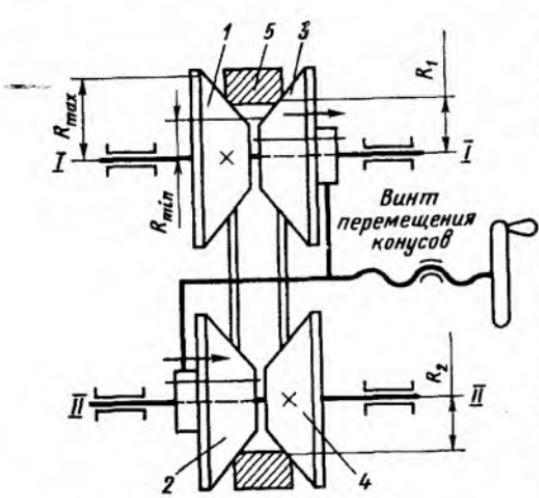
Схема вариатора с раздвижными конусами и стальным промежуточным кольцом
